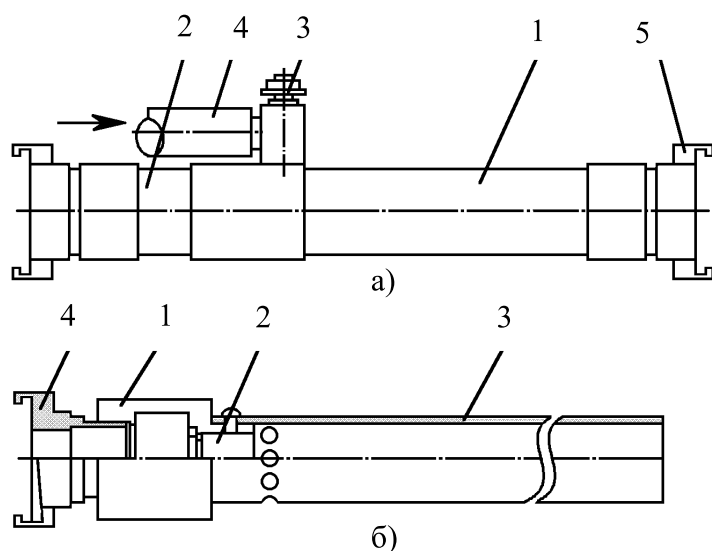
Оборудование пенно-воздушное ОВП-10: а – пеносмеситель: 1 – корпус диффузора; 2 – конфузор; 3 – дозирующий кран; 4 – всасывающий трубопровод; 5 – соединительная головка; б – ствол воздушно-пенный: 1 – корпус; 2 – диафрагма; 3 – направляющая труба; 4 – соединительная головка
